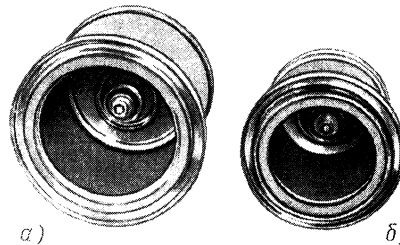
Высоковольтные изоляторы из порошкового материала для сварочных пушек с ускоряющим напряжением 60 кВ (а) и 30 кВ (б)
